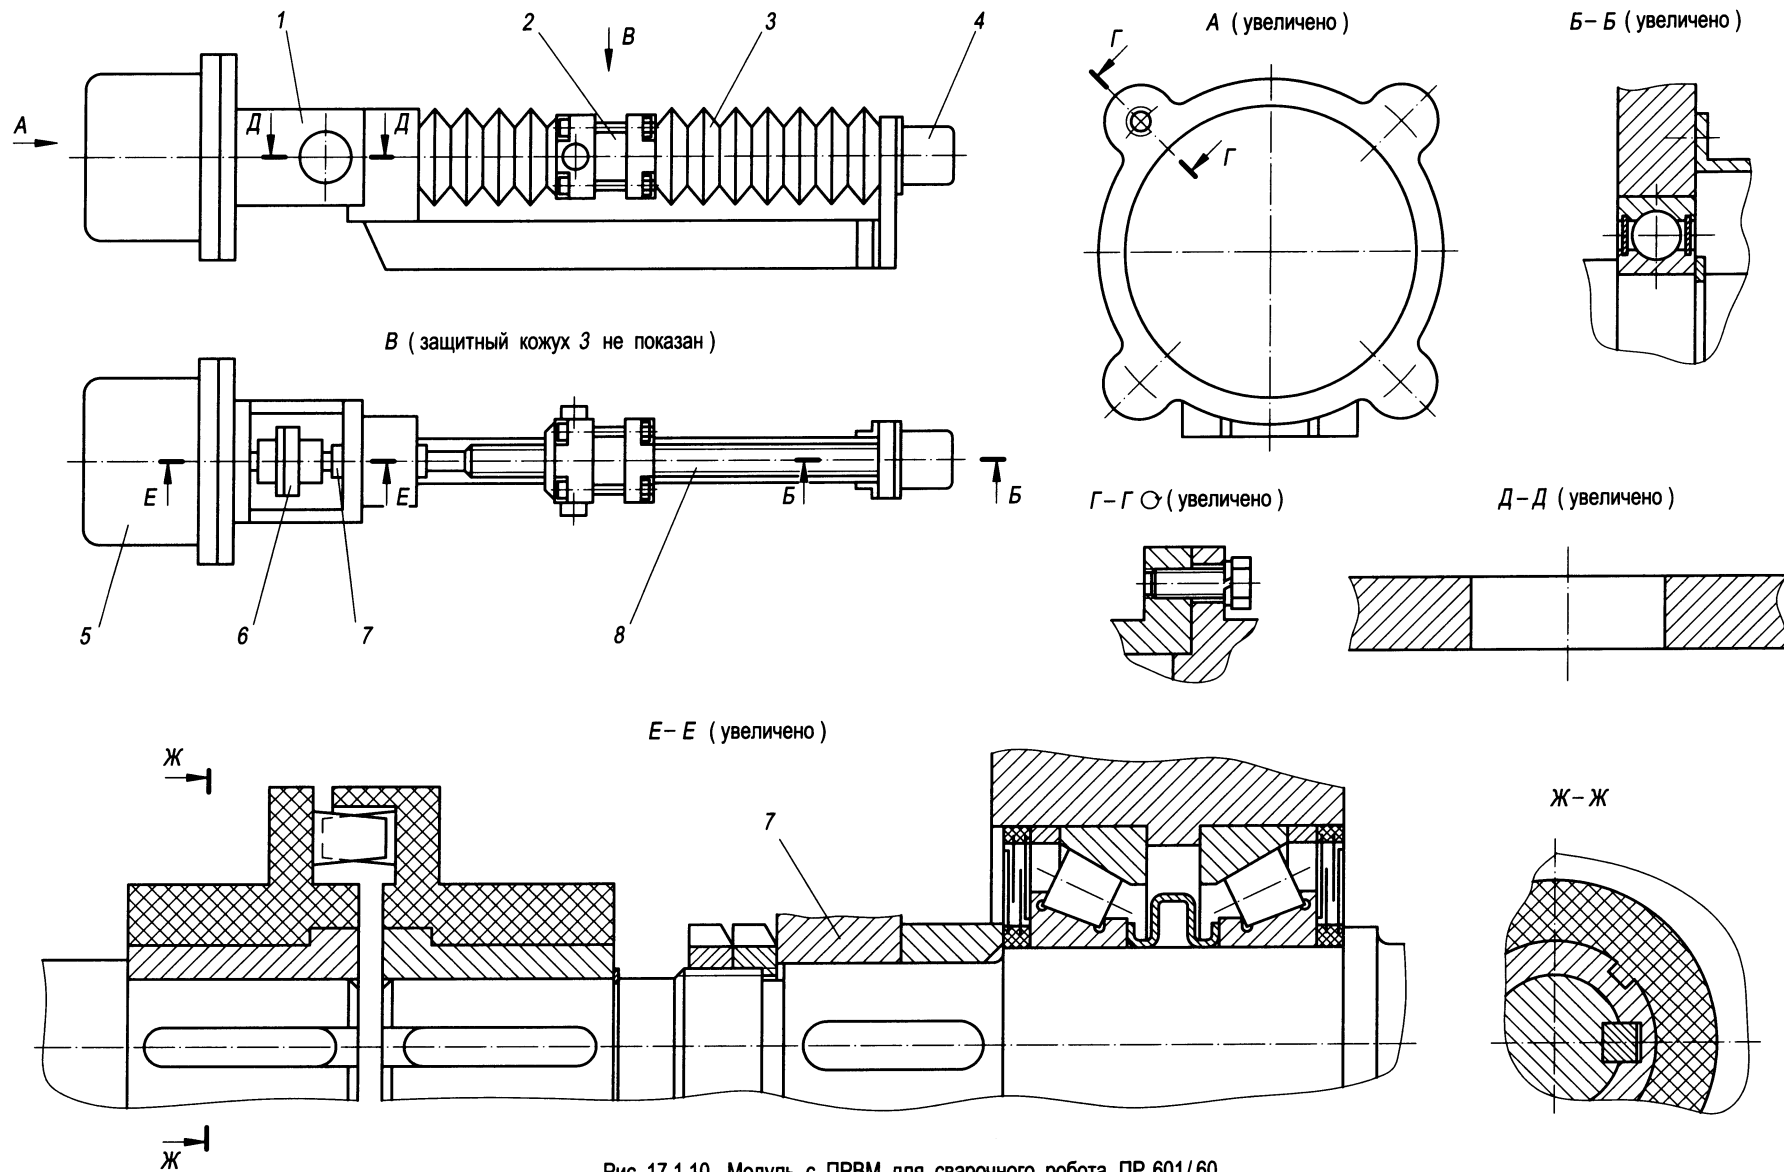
Модуль с ПРВМ для сварочного робота ПР 601/60
